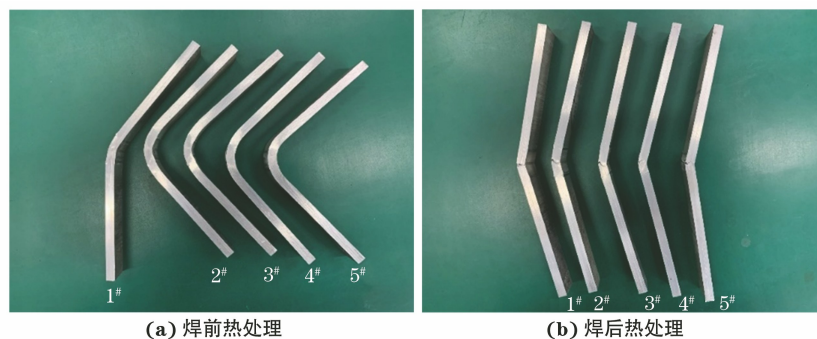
焊前和焊后热处理不同工艺制备得到焊接接头三点弯曲试样的宏观形貌
